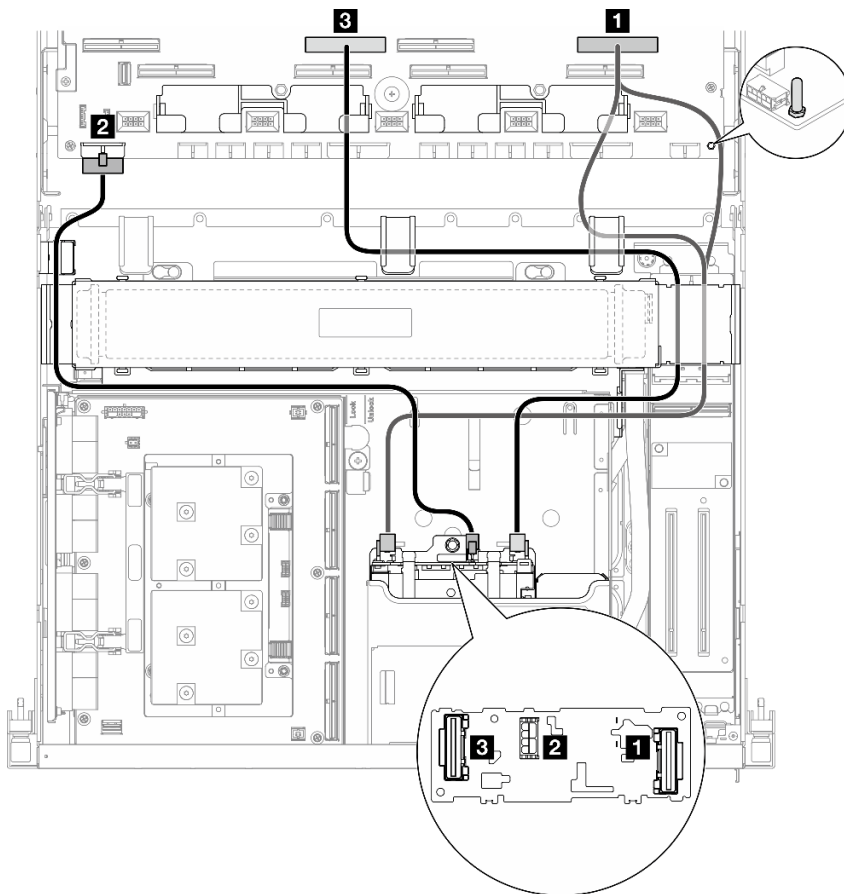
Disposición de los cables de la placa posterior de unidad E3.S
